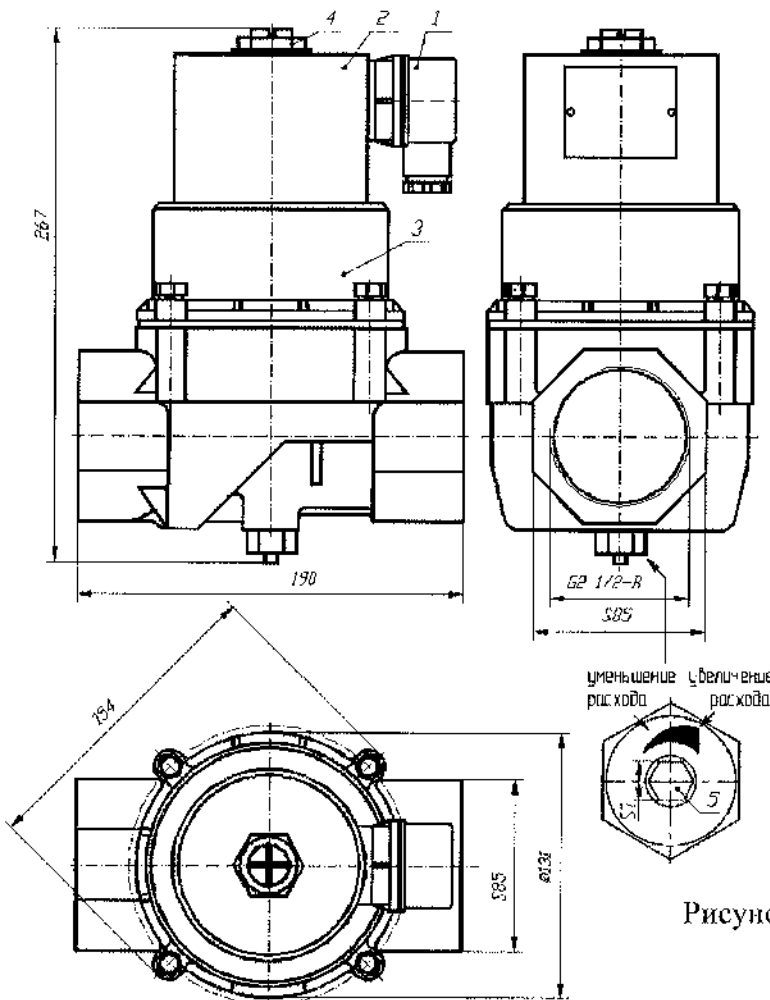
Габаритные и установочные размеры клапана КГЭЗ-50
